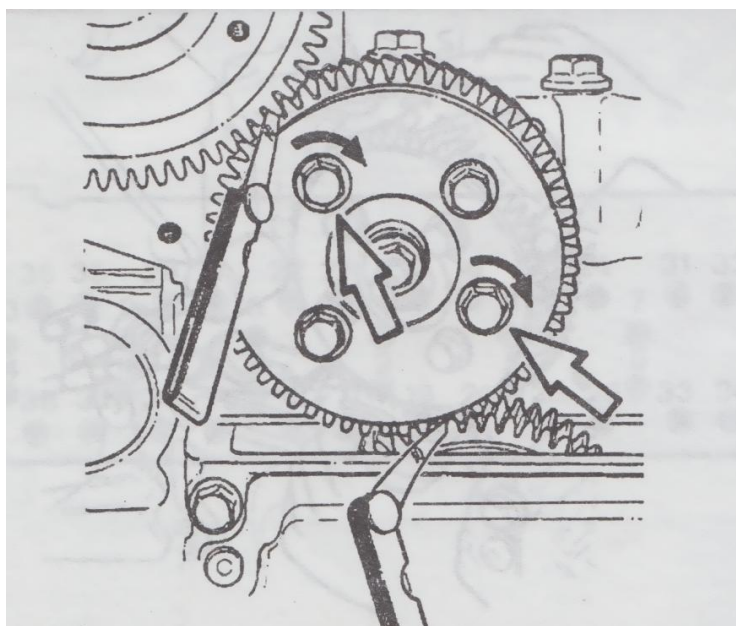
Установка щупов при регулировке промежуточной шестерни распределительного вала двигателя D12 Volvo
